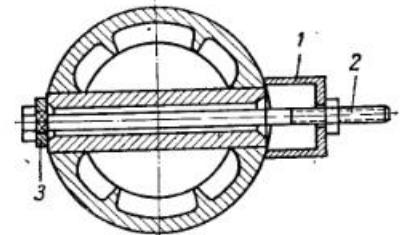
Приспособление для выпрессовки поршневого пальца:
